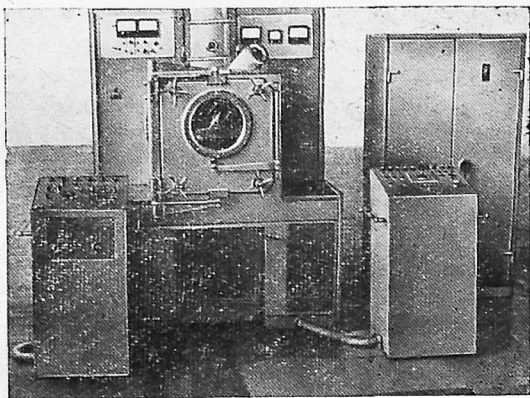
Установка УЭЛС-1 для электронно-лучевой сварки небольших деталей.
